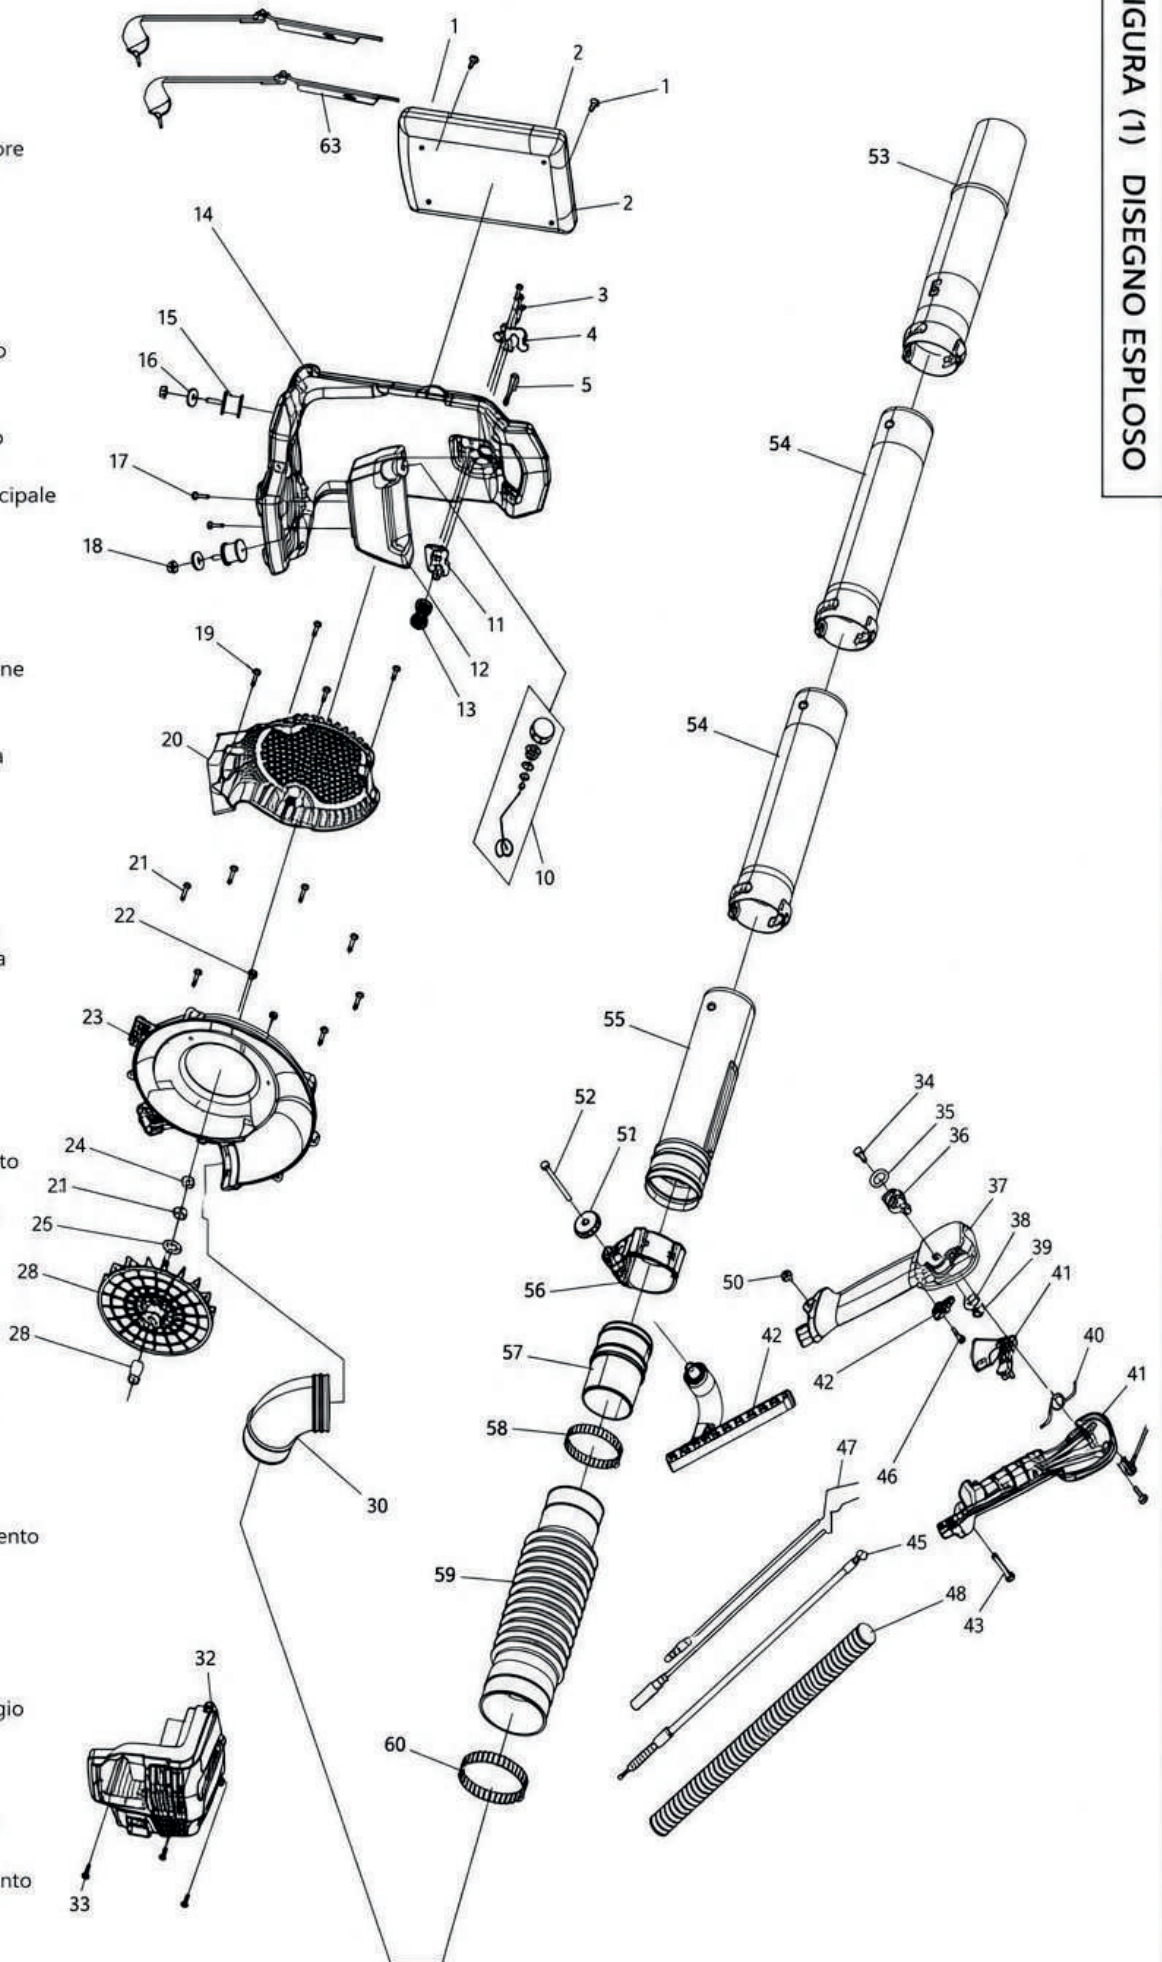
FIGURA (-) DISEGNO ESPLOSO DEL MOTORE
